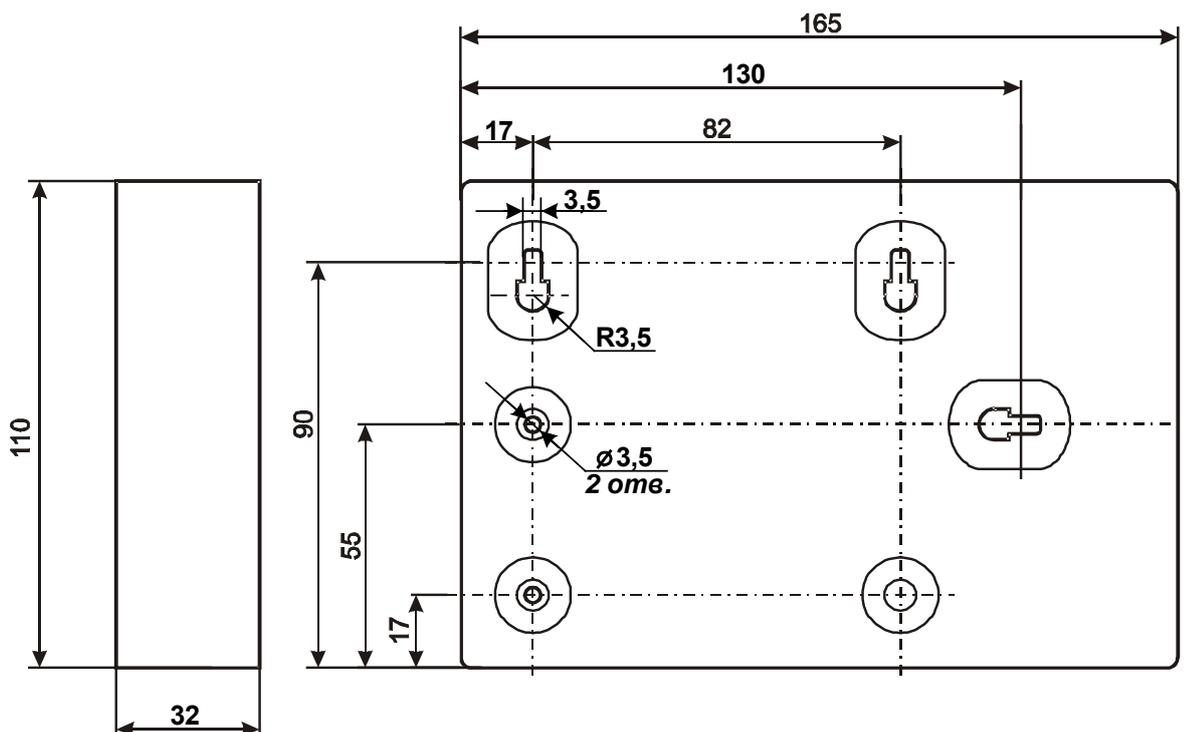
Габаритные и присоединительные размеры корпуса МПТ
